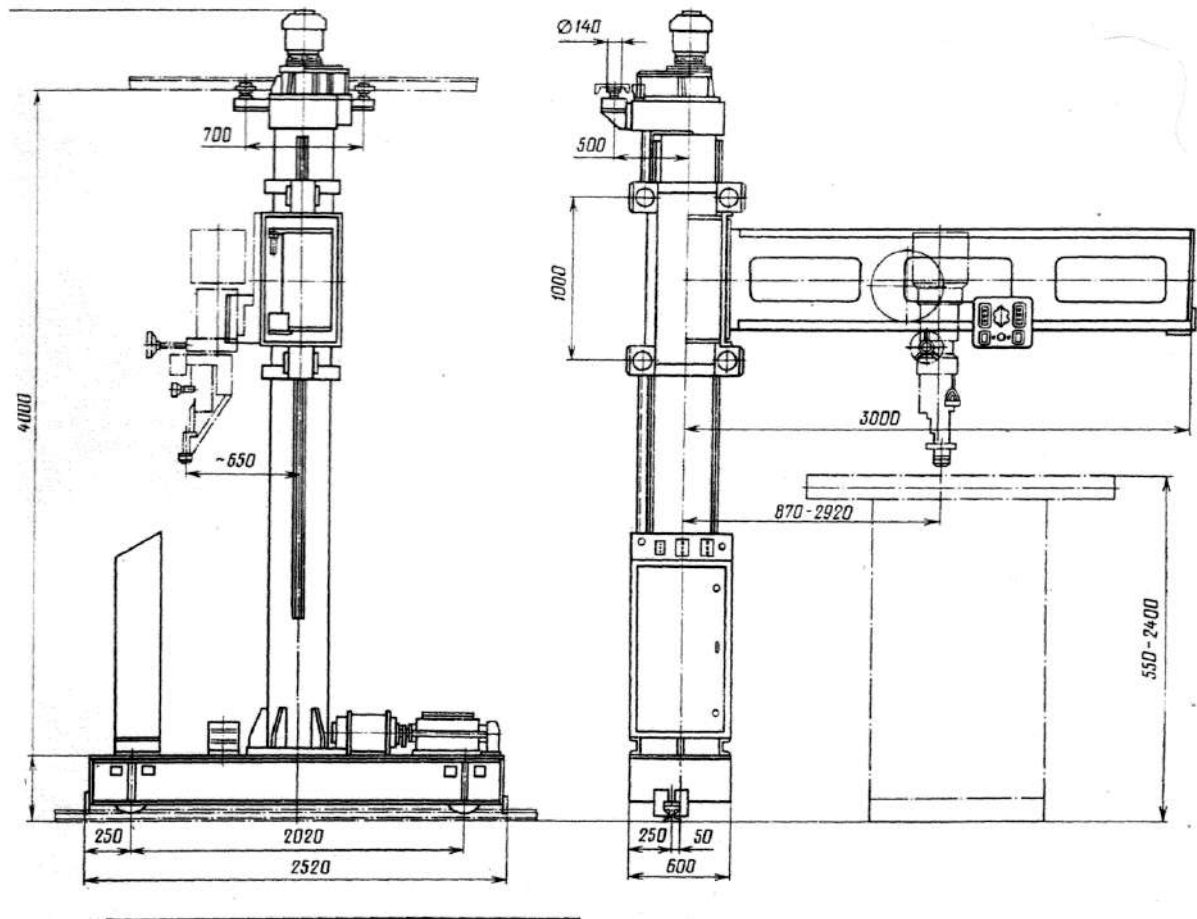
Загальний вид велосипедного візка ВТ-2 [14].
